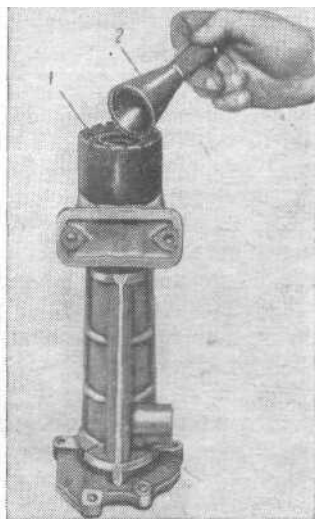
Запрессовка сальников в горловину удлинителя коробки передач при помощи оправки
